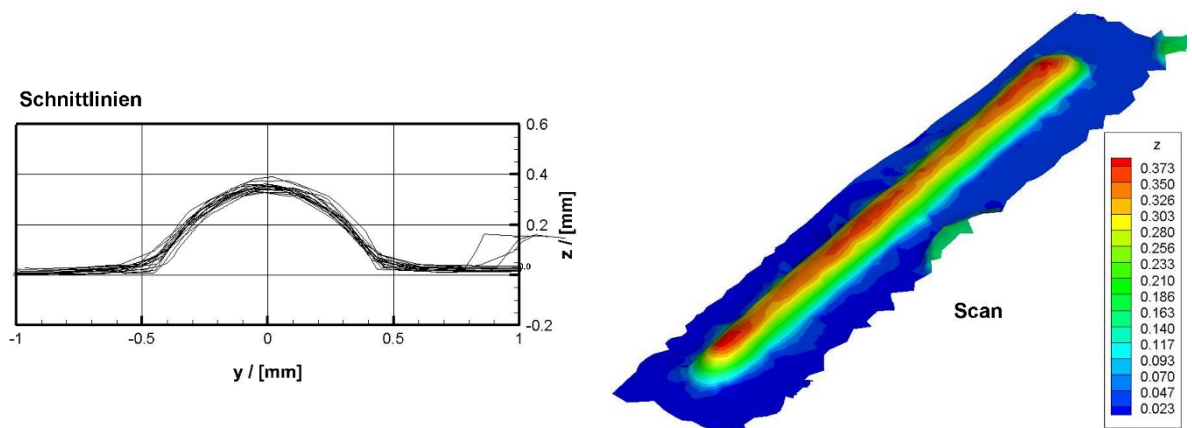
Analyse der Geometrie einer laserauftragsgeschweißten Spur durch optisches Scannen
